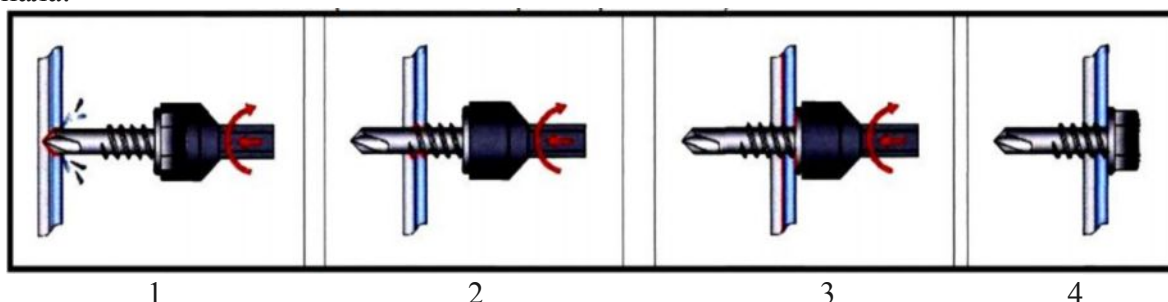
Выполнение соединения на самосверлящем самонарезающем винте: 1 – сверление, 2 – нарезка резьбы, 3 – затяжка, 4 – готовое соединение.
